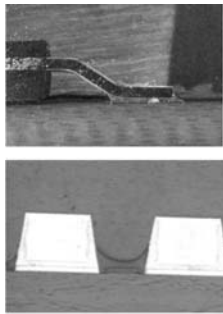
安装在 TJ5A PCB 模板上的 TO-263 THIN 封装的 X-射线分析
